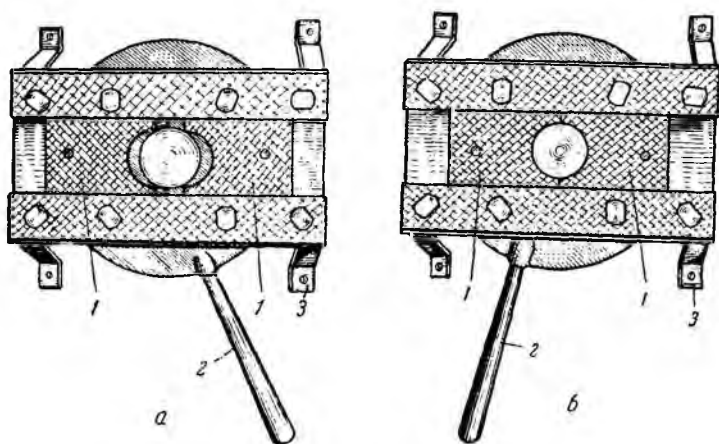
Станок для обжима очковых обоек противотога (вид сверху):
